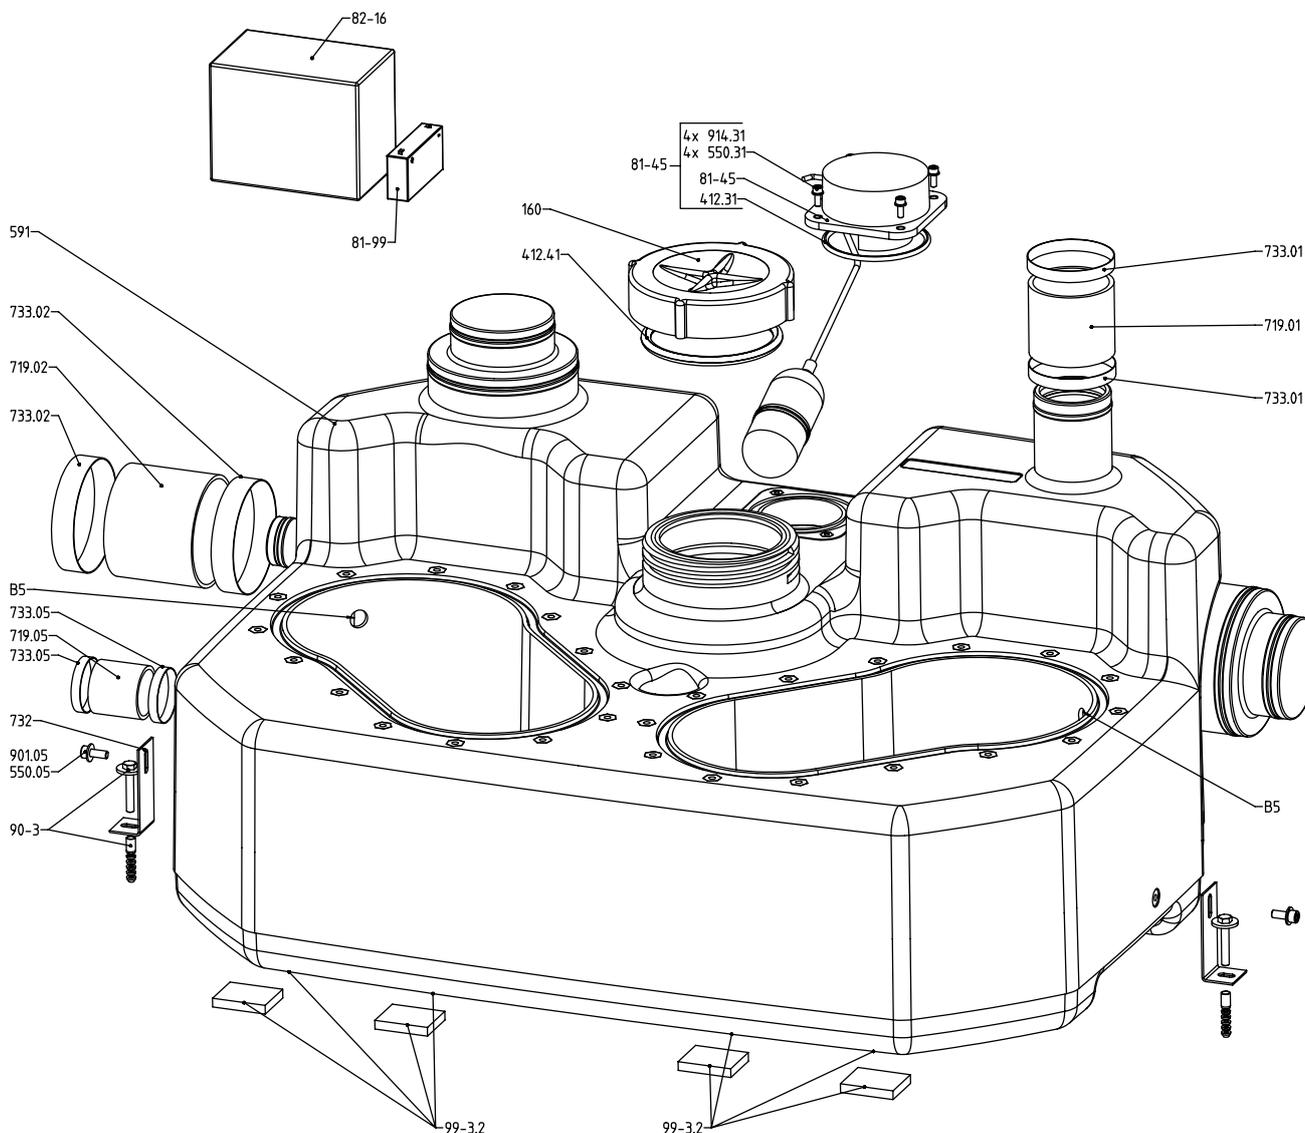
Деталировочный чертеж mini-Compacta UZS150 - сборный резервуар
